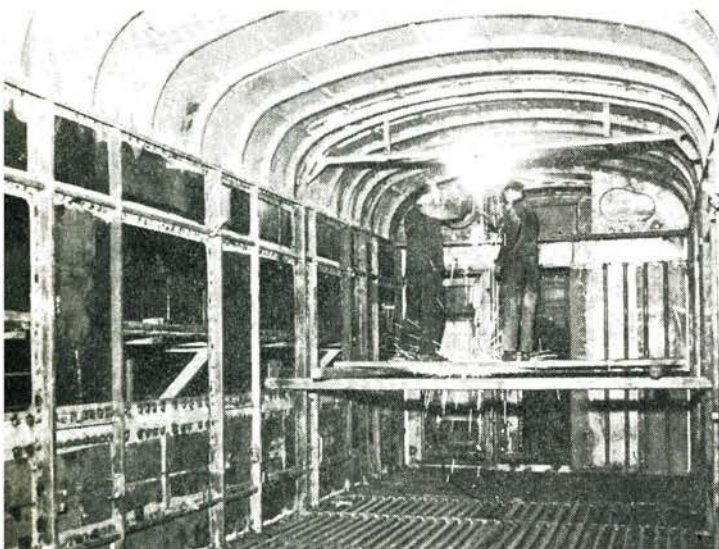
Schweißarbeiten an der Stirnwand eines Wagenkastens; deutlich sind die Punktschweißstellen der einzelnen Längswandbleche erkennbar
